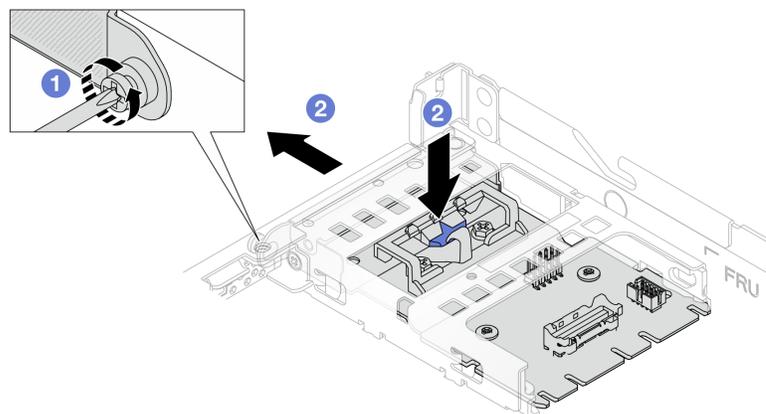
Entfernen der hinteren OCP-Interposerkarte
